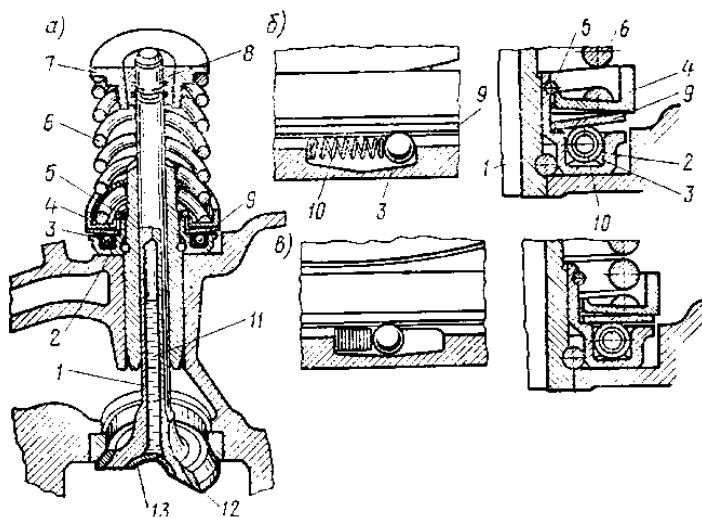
Випускний клапан двигуна ЗИЛ-130 з механізмом його обертання біля осі
